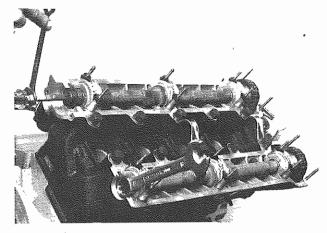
Ruotare gli assi a camme Rotate camshafts
